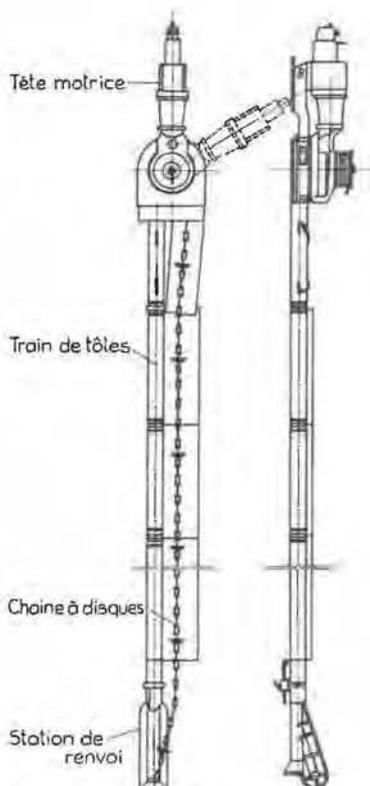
Vue d'ensemble du transporteur freineur à disque.
